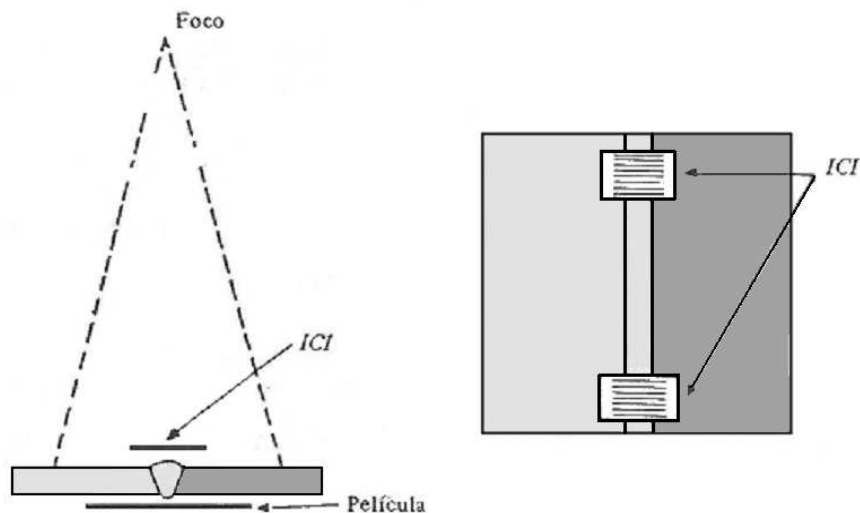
Montaje para la toma radiográfica al cupón soldado.
